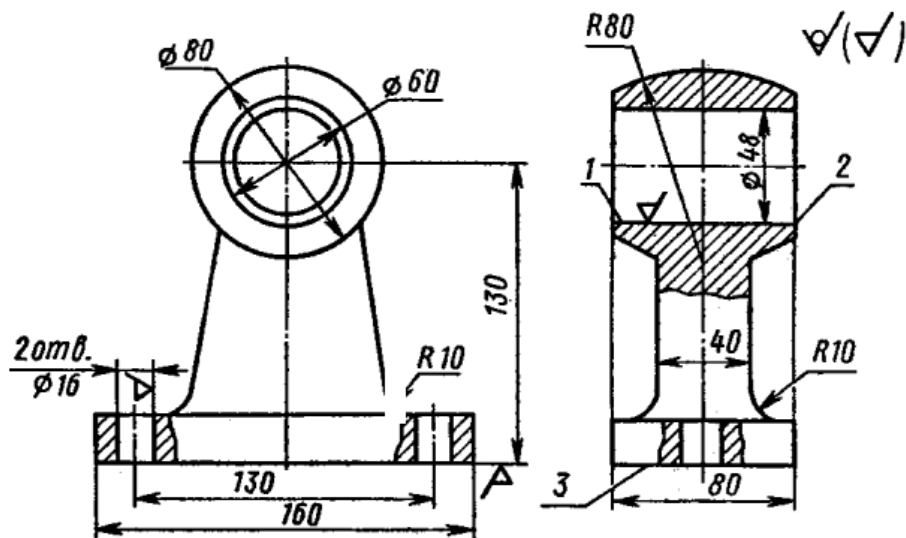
Корпус (материал – чугун ВЧ 60)
